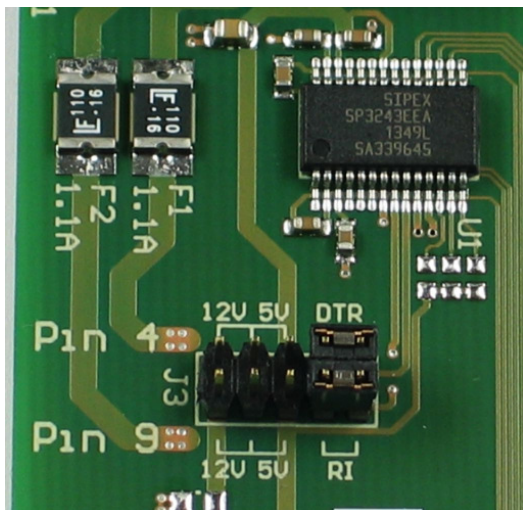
Jumperpaar J3 auf dem RS232-Schnittstellenmodul
